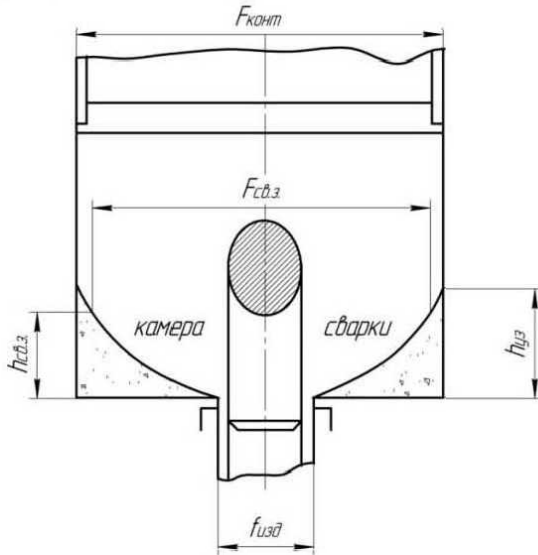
Характерное сечение камеры сварки матрицы
